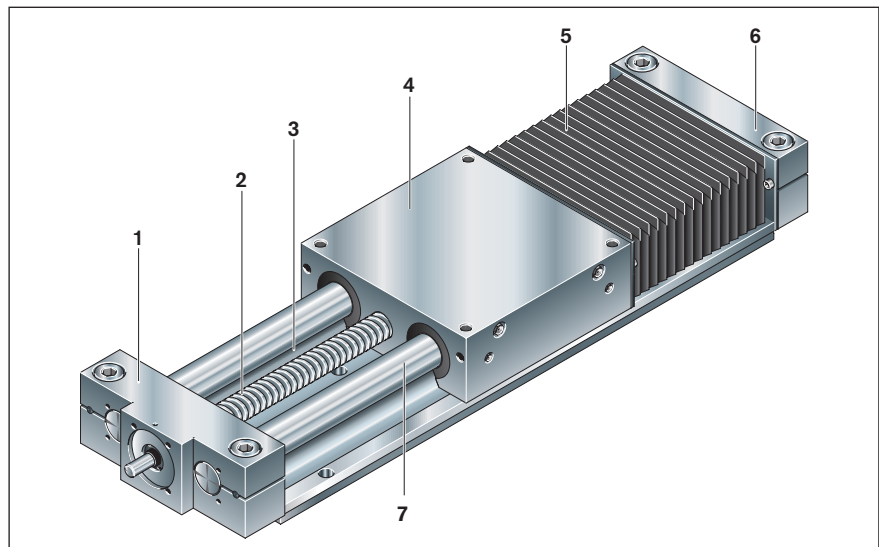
Bestandteile des Linearschlittens mit Kugelgewindetrieb
